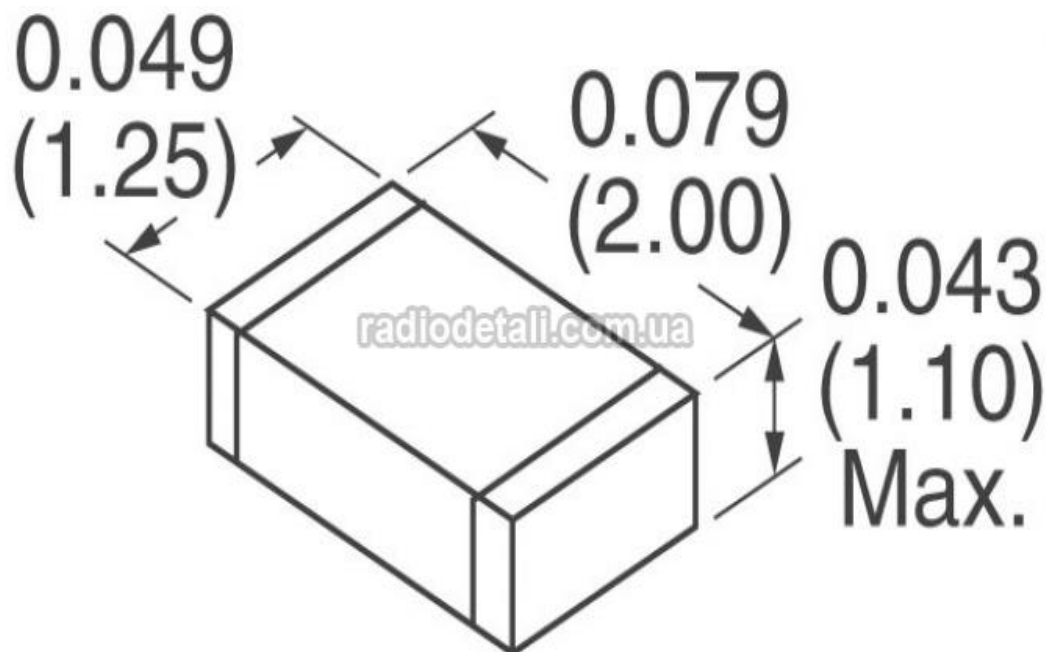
Габаритні розміри резисторів RC0805FR
